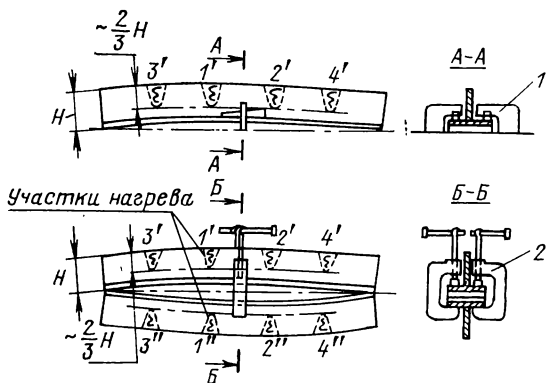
Схема правки сварных тавровых балок нагревом с принудительной посадкой.
